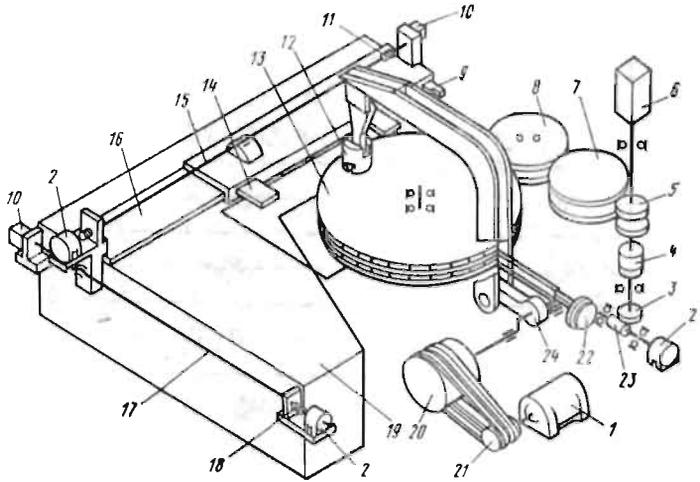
Кинематическая схема координатно-револьверного пресса с программным управлением
